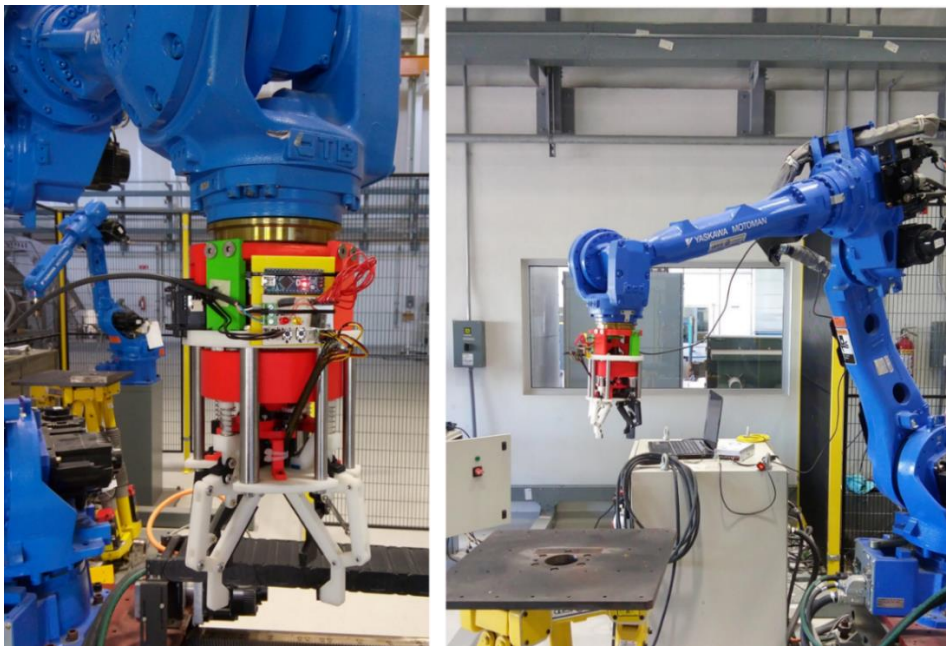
Gripper reconfigurable de 4 dedos montado en robot industrial.
